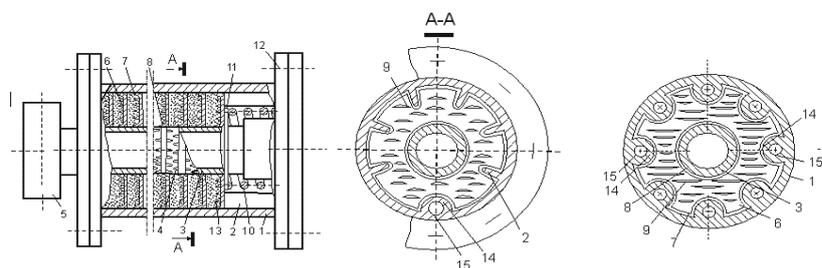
Схема конструкции генератора-абсорбера с внутренним подвижным оребрением: фрагменты пластин: 1- корпус цилиндрический, 2-ребро продольное, 3-трубка перфорированная, 4-отверстие овальное, 5- хладопровод, 6- пластины подвижные лепестковообразные, 7 - буртики срезные внутренние, 8 –буртики срезные наружные, 9- насечки горизонтальные, 10 - пружина винтовая, 11 – шайба подвижная, 12 – фланец корпуса, 13 - абсорбент,
